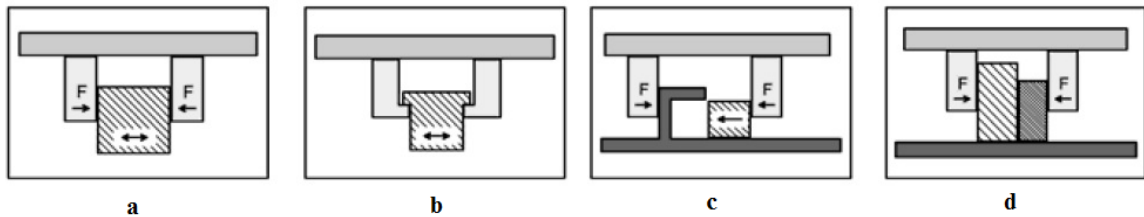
Typy upínání obrobků: a – posunutí obrobku povolené, b- posunutí obrobku zakázané, c – upínání pevně ustaveného obrobku, d – upínání flexibilního obrobku [1]
